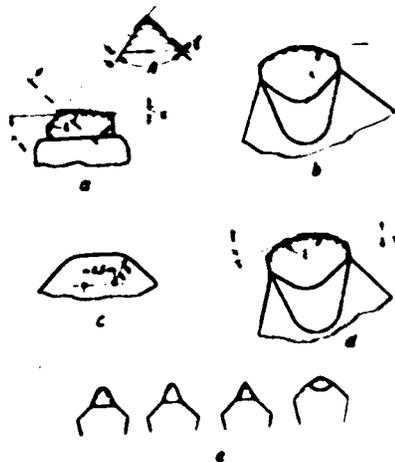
Verschiedene Schneidformen von Diamantwerkzeugen
